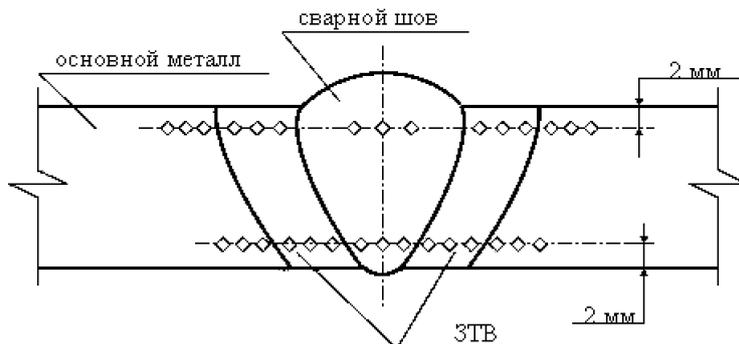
Схема замера твердости по Виккерсу в различных зонах сварного соединения
